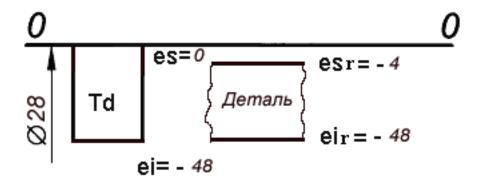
Графическое представление поля допуска и действительных размеров детали
